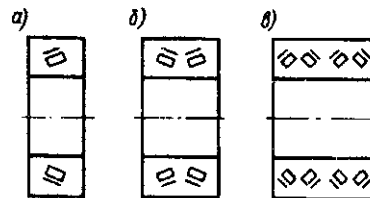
Роликовый подшипник радиально-упорный: *a* — однорядный; *b* — двухрядный; *в* — четырехрядный
